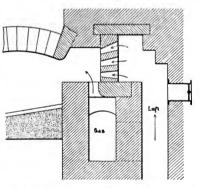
Gasrohrschweißofen mit Halbgasfeuerung.
